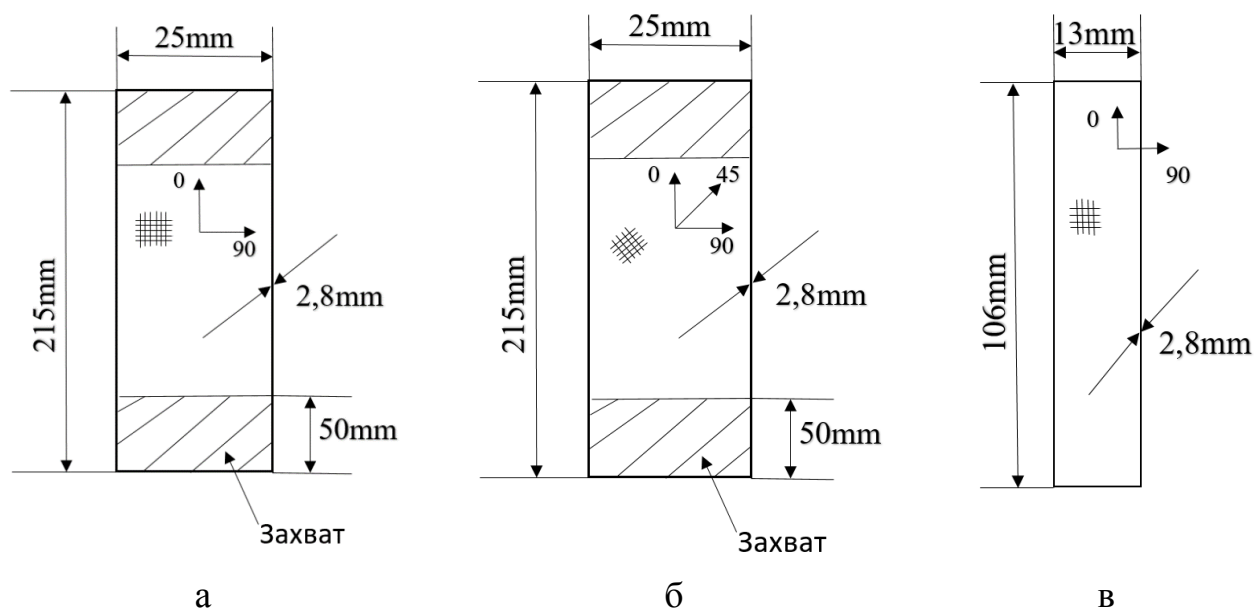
Эскизы образцов: а) образец для испытания по ASTM D3039; б) образец для испытания по ASTM D3518; в) образец для испытания по ASTM D7264.
